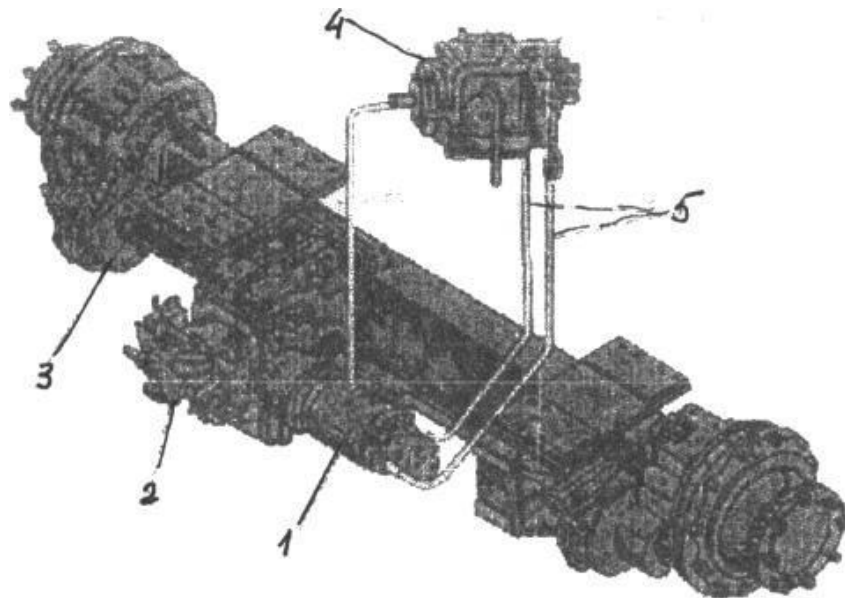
Мост ведущих колес с гидростатическим приводом: 1 - гидромотор; 2 - коробка диапазонов; 3 - бортовой редуктор; 4 – гидронасос; 5 - гидролиния.
